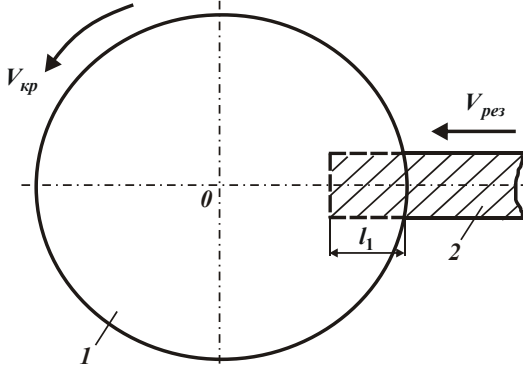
Расчетная схема процесса шлифования прямолинейного образца, движущегося по нормали к рабочей поверхности круга: 1 – шлифовальный круг; 2 – образец.
